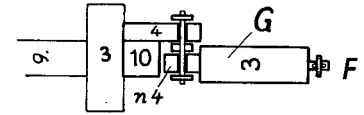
Das Gegengewicht G, welches die Sperre geschlossen hält, solange der Hebel H sie nicht öffnet.
